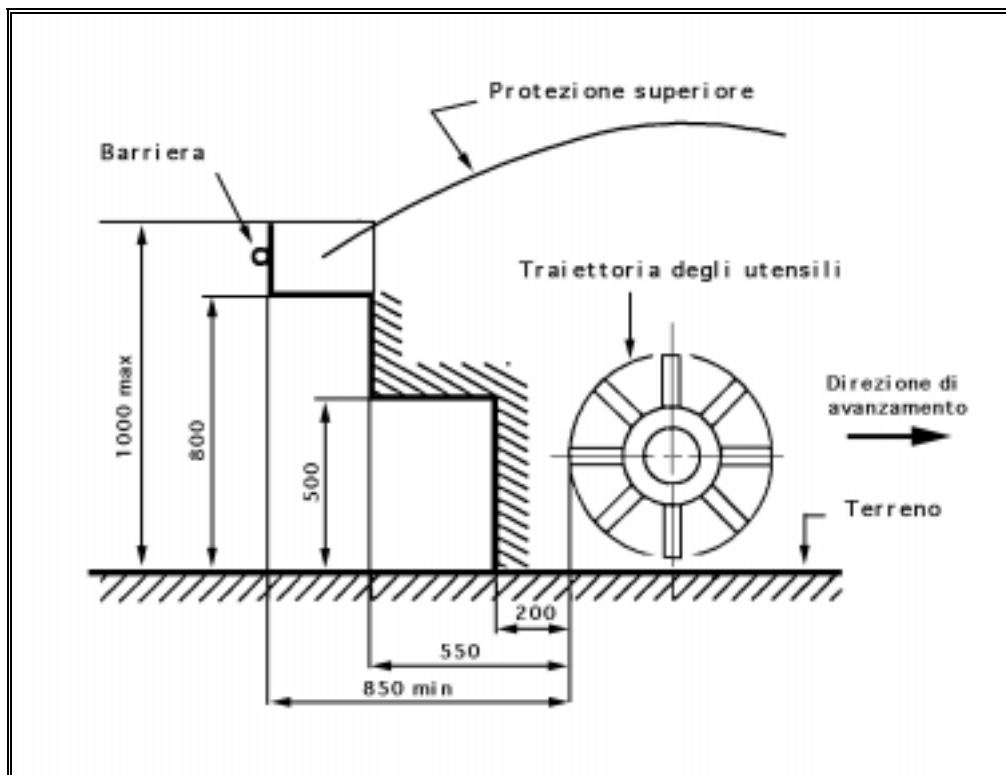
Dispositivo di condizionamento - Protezione superiore nel caso in cui il bordo posteriore è localizzato tra 800 mm e 1000 mm dal terreno
